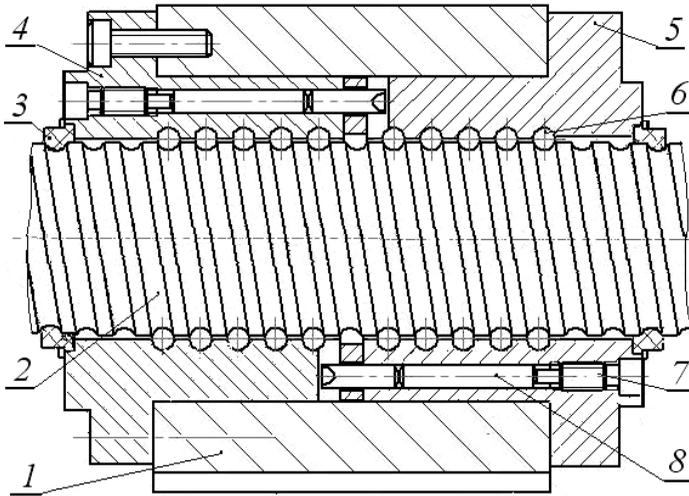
Передача винт-гайка качения с поворотом гайки 5 для регулирования натяга регулировочными штифтами 8, расположенными в обеих гайках
